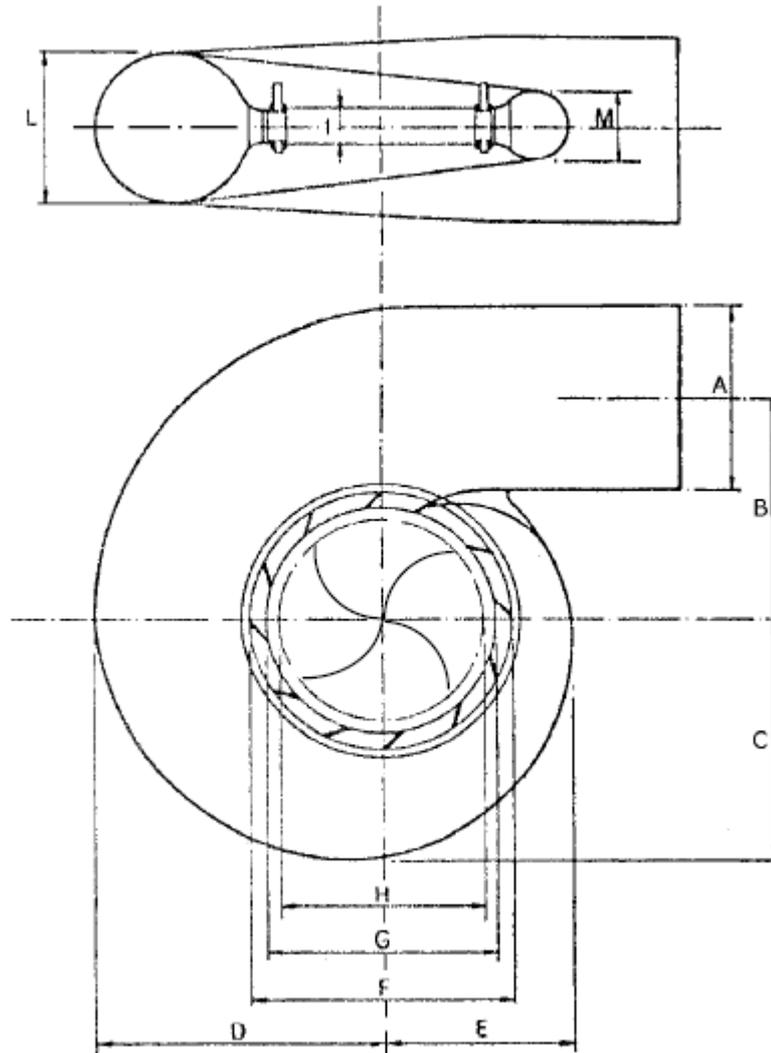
Alzado y planta del dimensionamiento de la cámara espiral.
